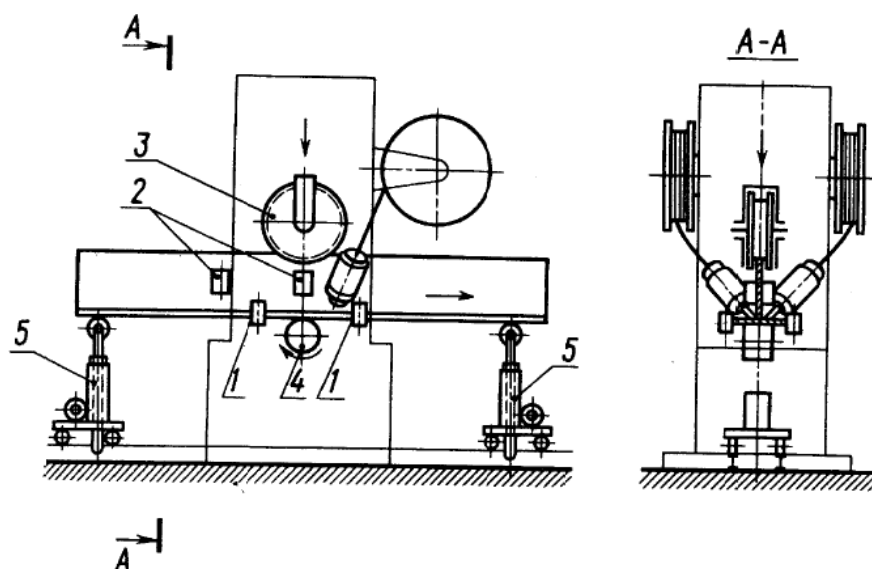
Схема станка для сварки балок таврового сечения
